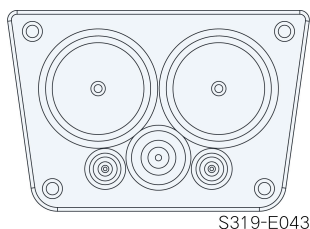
Placa de vedação para um cabo por fase com cabo multipolar
